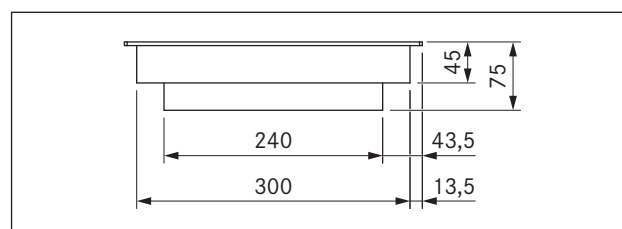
Dimensões do aparelho CKCB, vista frontal
